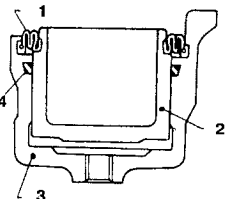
Расположения поршня, цилиндра и уплотнений (См. Раздел 5)
